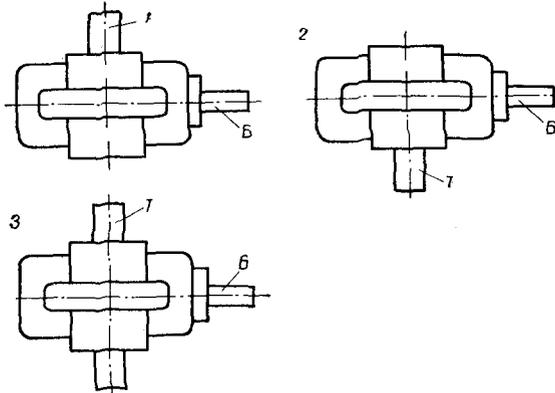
Схемы сборок (1—3) редукторов РЧН и РЧП:
